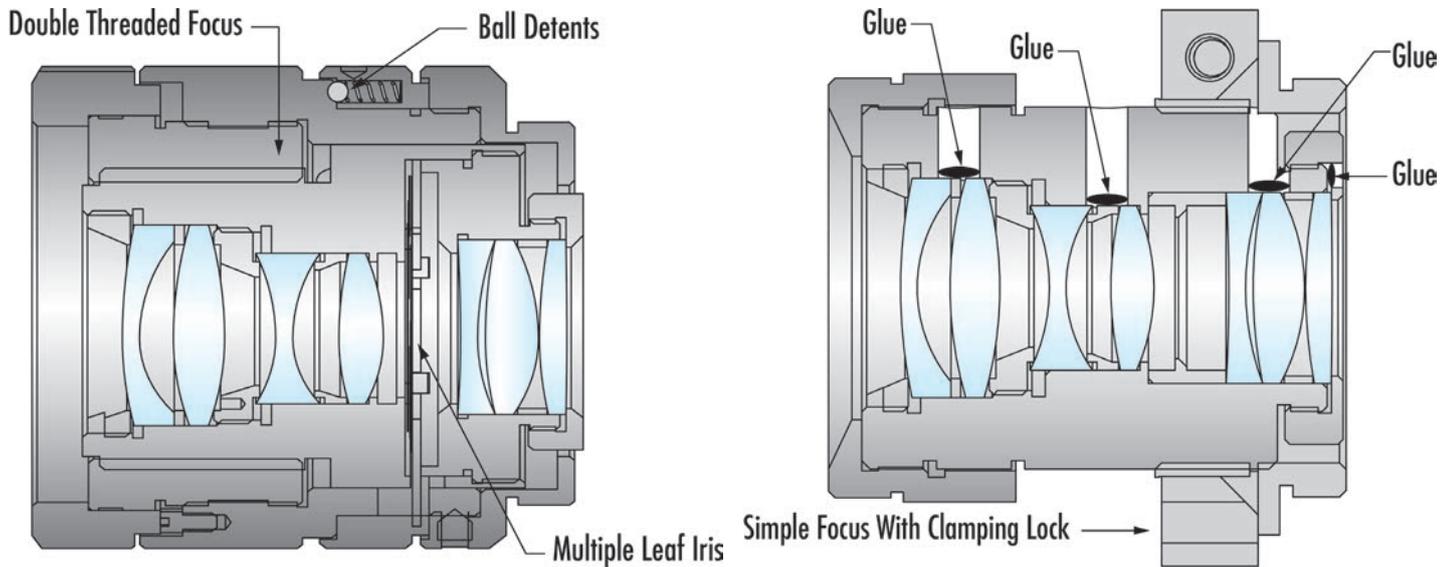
+b | Optomechanisches Layout eines C-Mount Standardobjektivs (l.). Die gleiche Optik in deutlich robusterer Ausführung, mit verklebter Optik und vereinfachter Mechanik (r.).
